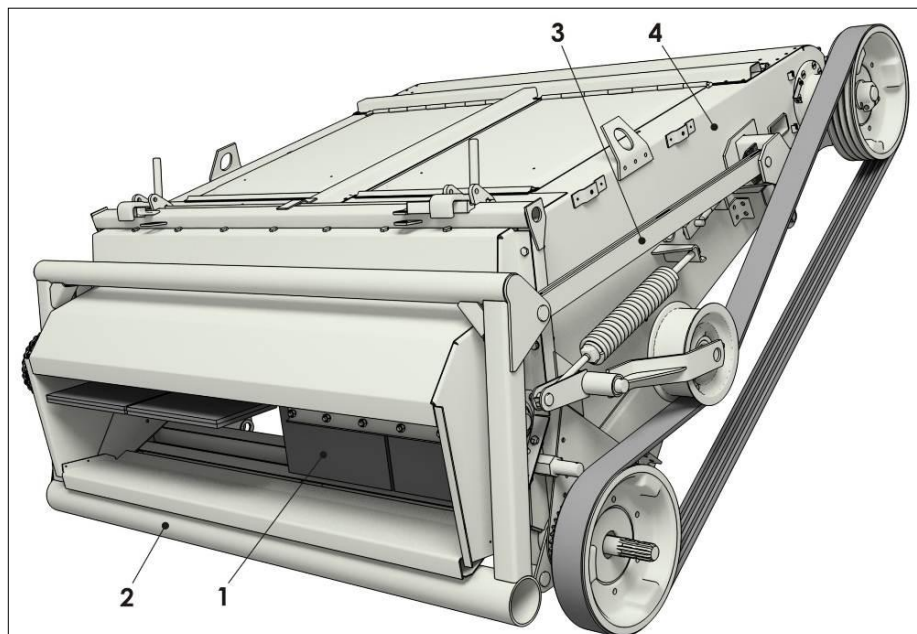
Механическая регулировка отрывочных пластин русла
